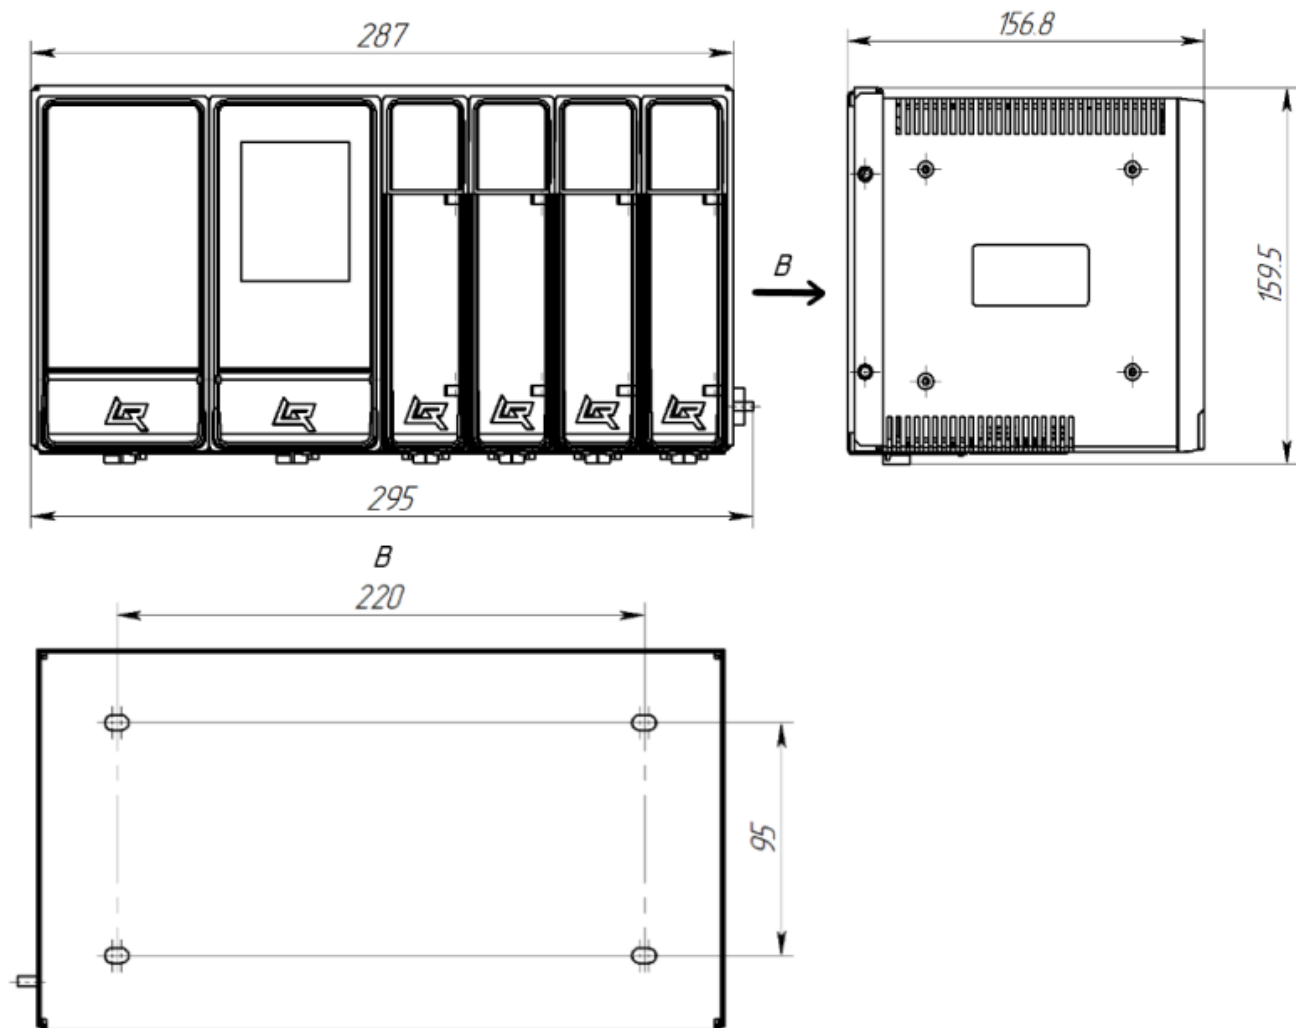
Габаритные и присоединительные размеры сборки контроллера на шасси SH-08 с модулями в пластмассовом корпусе
